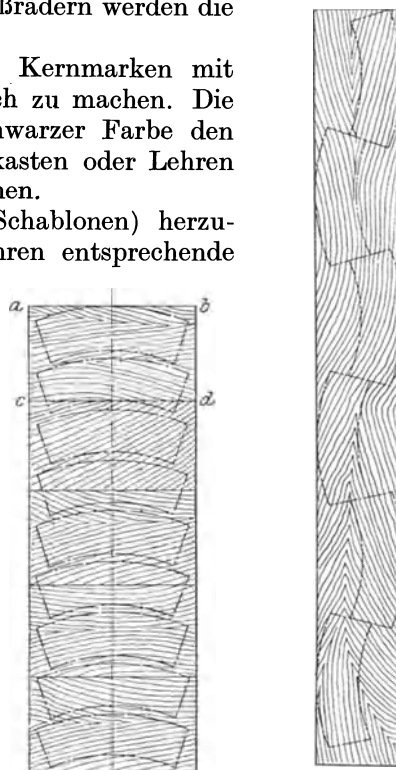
Sparsames Zuschneiden des Holzes.      Abb. 906. Beispiel für Holzverschwendung.
